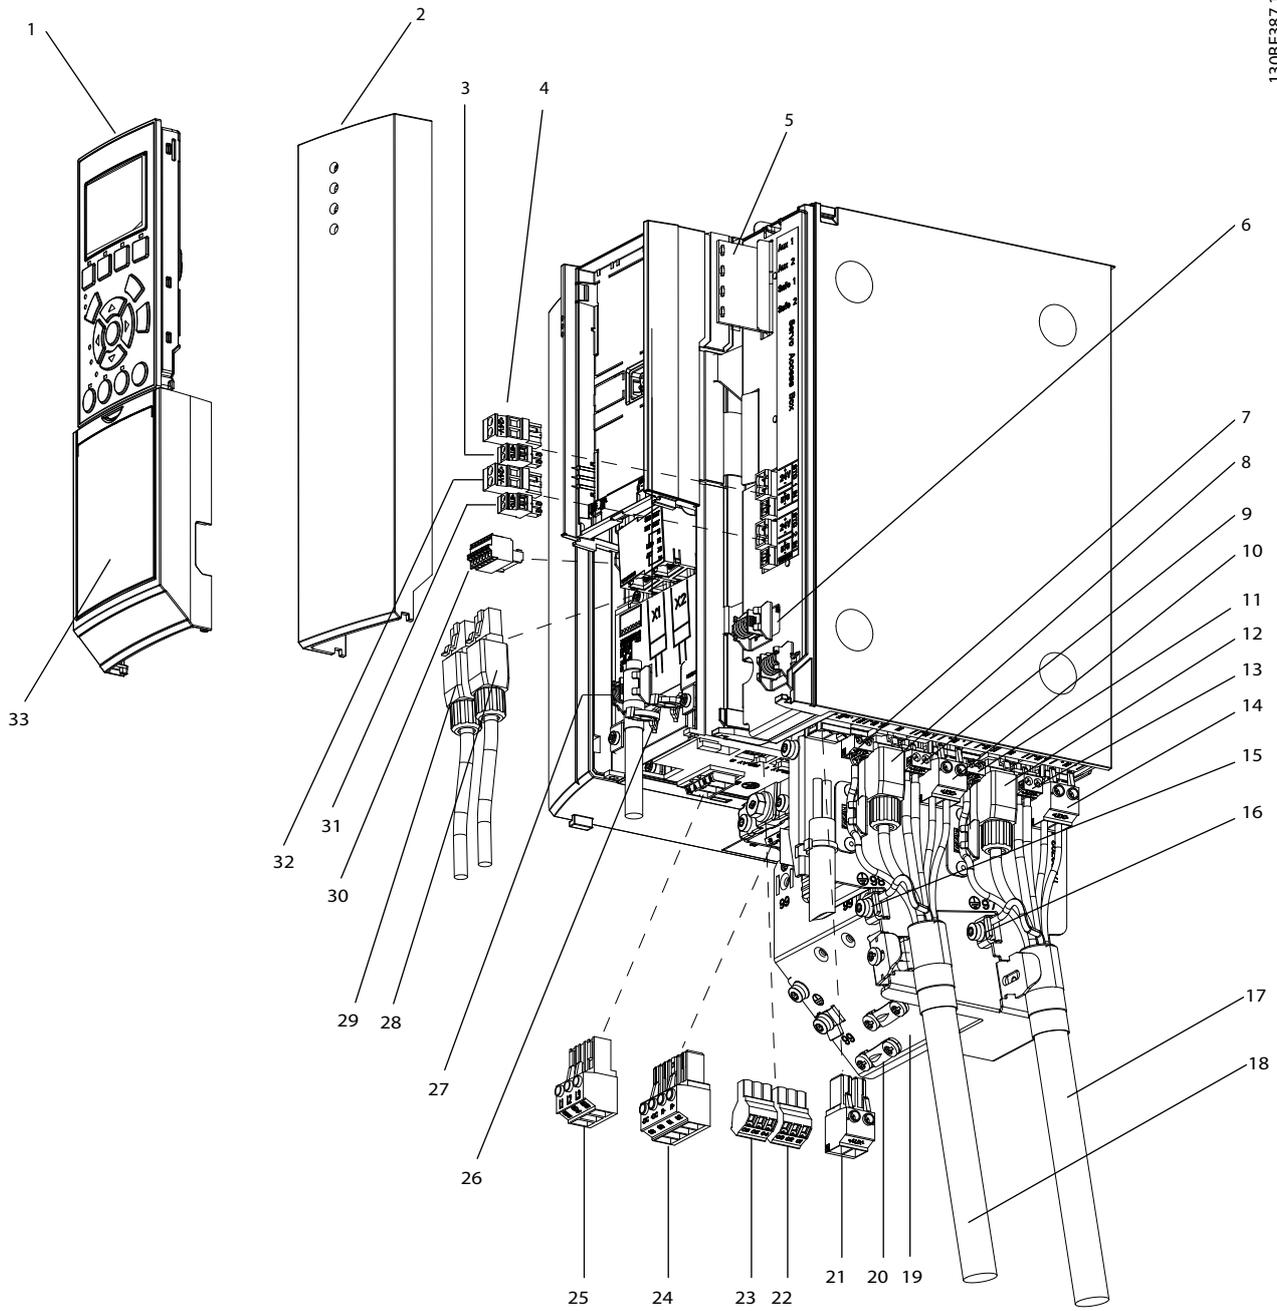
Explosionszeichnung der Servo Access Box
